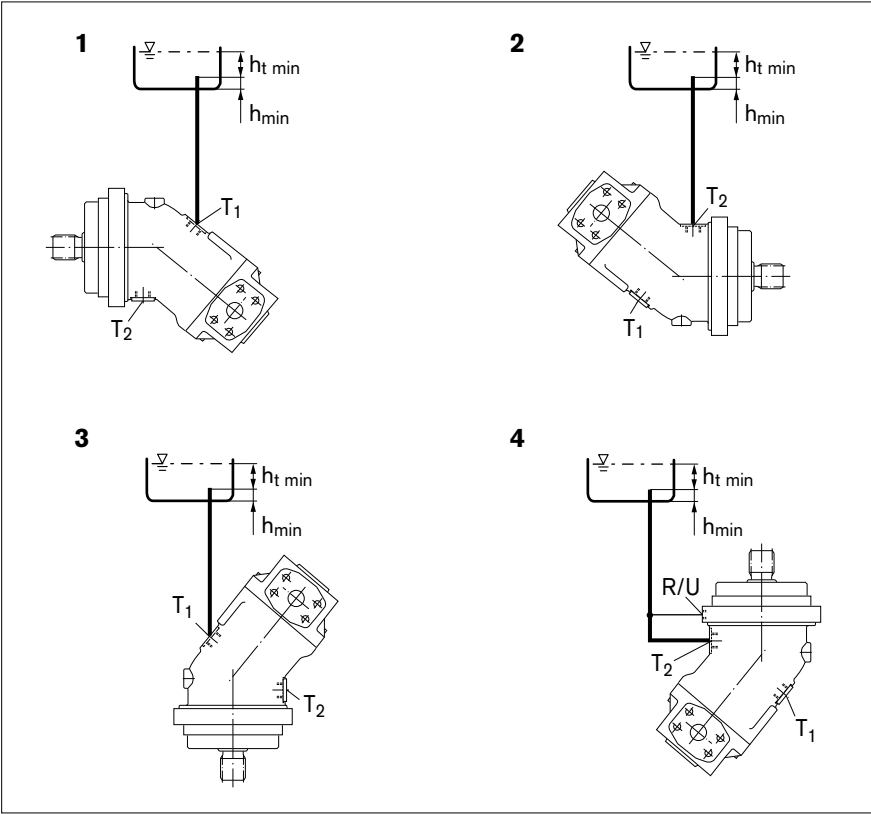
Montaje bajo el tanque con posiciones de montaje 1–4
